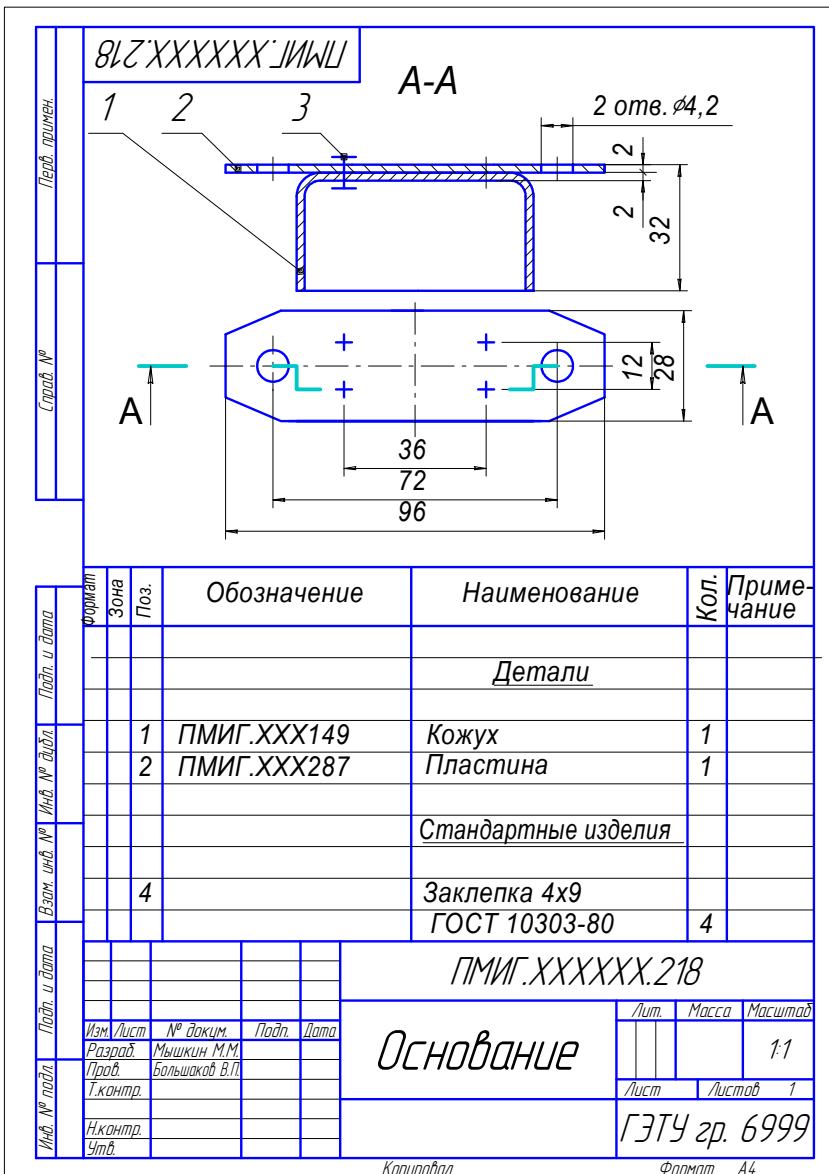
Пример выполнения сборочного чертежа изделия с клепаными соединениями
